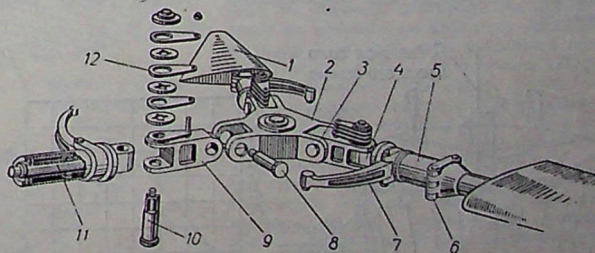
1 — лопасть, 2 — корпус втулки, 3 — горизонтальный шарнир, 4 — вертикальный шарнир, 5 — осевой шарнир, 6 — узел крепления лопасти, 7 — поводок управления лопастью, 8 — палец горизонтального шарнира, 9 — корпус шарниров, 10 — палец вертикального шарнира, 11 — палец осевого шарнира, 12 — детали фрикционного демпфера.
